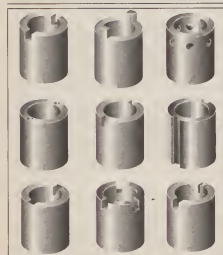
Варианты заготовок для изготовления гаек блокиратора «Кубик».
